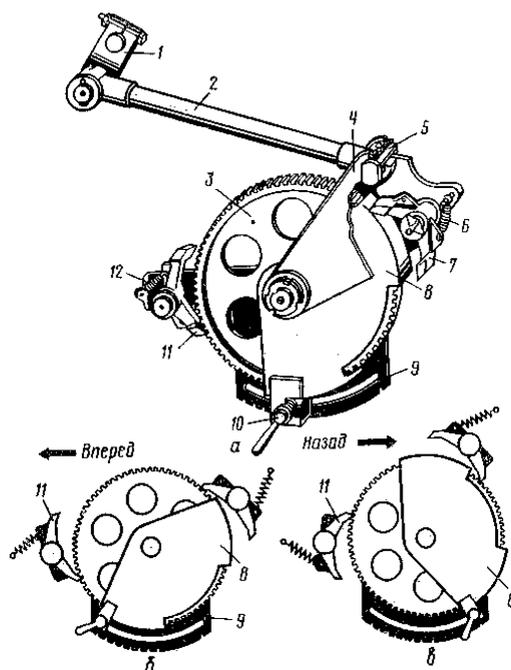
Устройство механизма (а) привода подающего транспортера кормораздатчика КТУ-10А при движении вперед (б) и. назад (в):
